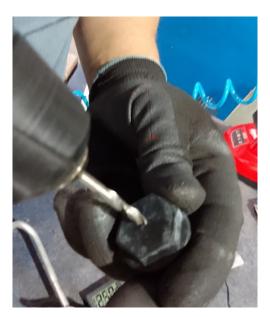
Furação central do MP0782- NIPLE DRENO 1/2"BSP
